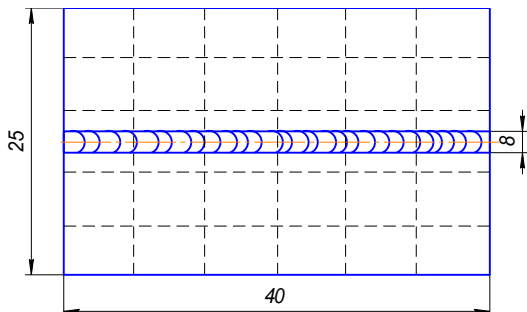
Схема образцов для контроля напряжений в сварном образце
